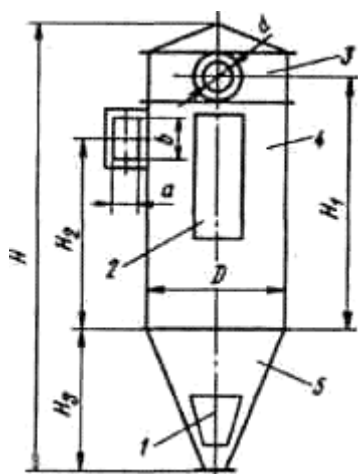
Фильтр типа РЦИ: 1 — люк; 2 — камера чистого воздуха; 4 — корпус; 5 — днище.
